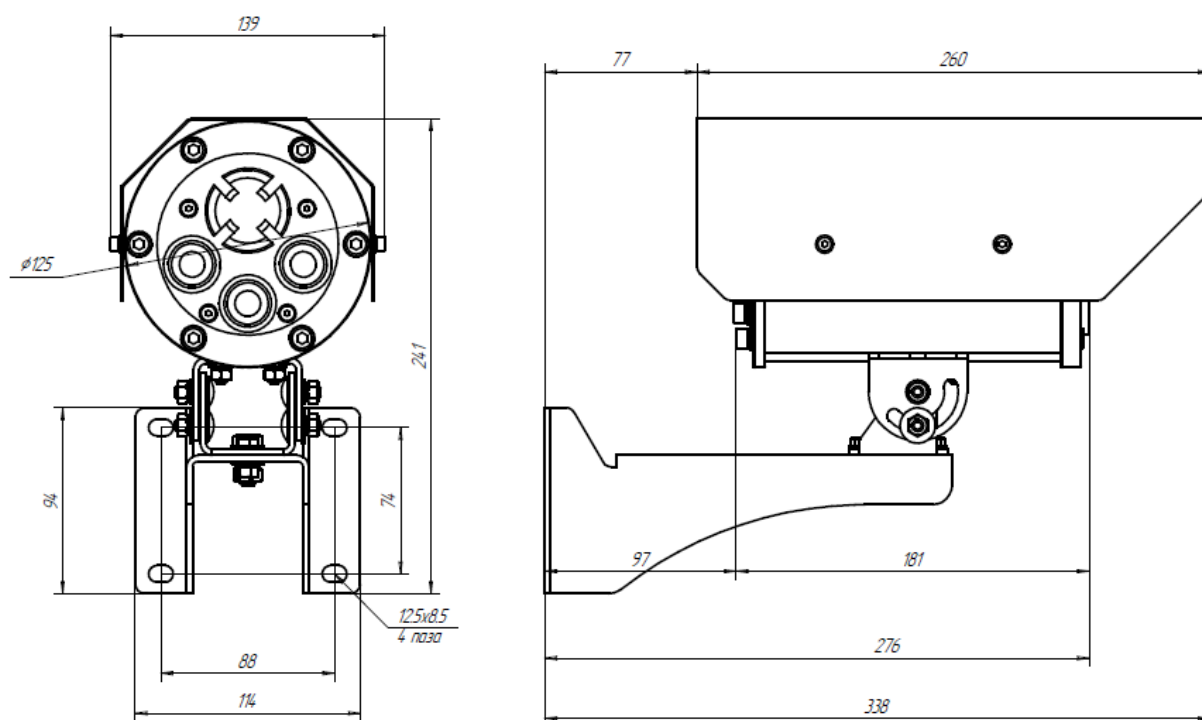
Габаритные размеры извещателя с крепежно-юстировочным устройством
